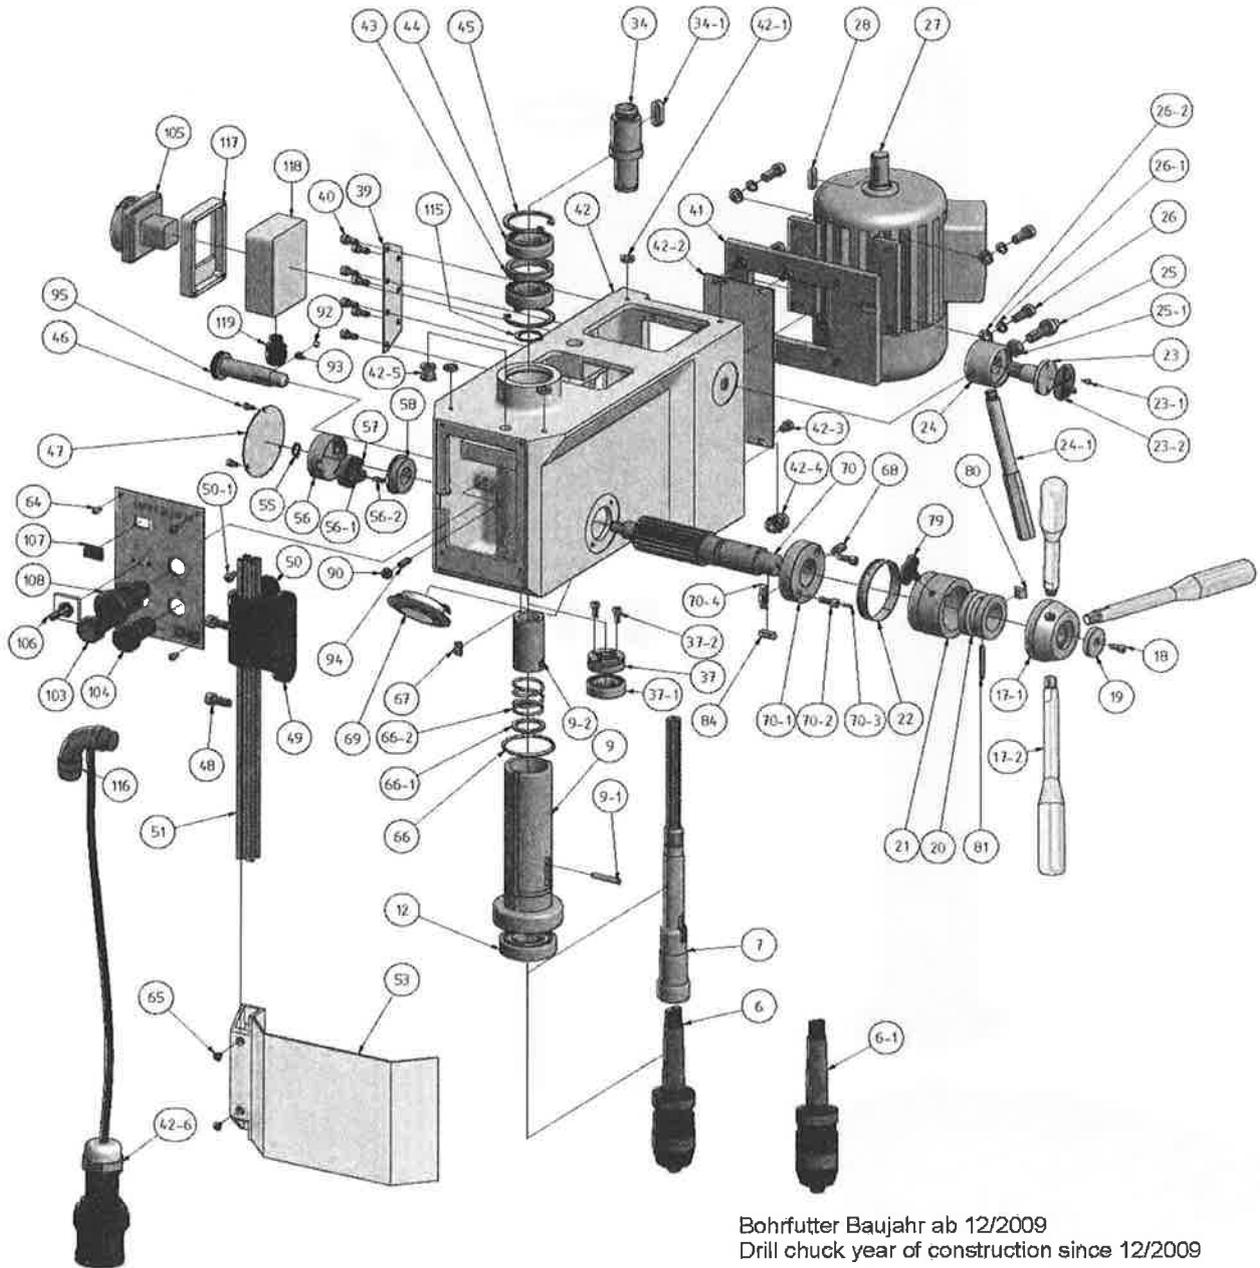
Bohrkopf B28H - Drilling head B28H
